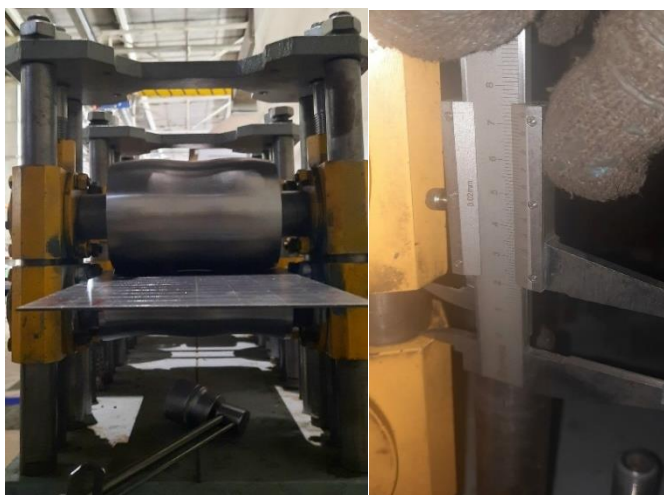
Проверка контакт заготовки с формовочными валками в клетки 1.ОК
